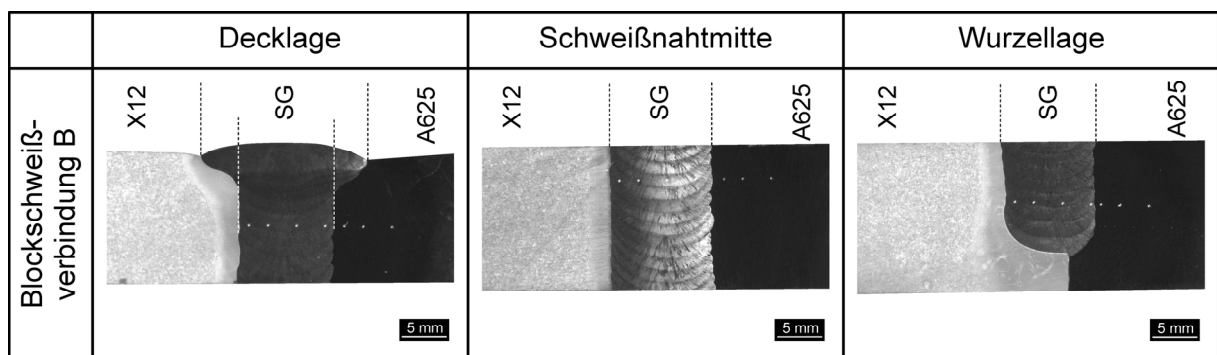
Decklage, Schweißnahtmitte und Wurzellage der BSVB, Makroaufnahmen, Ätzmittel V2A-Beize
